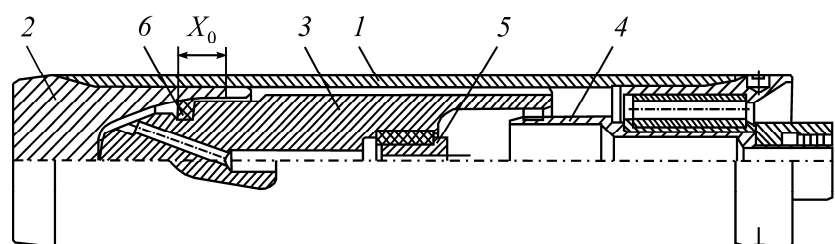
Общий вид пневмомолота: 1 — корпус; 2 — наковальня; 3 — ударник; 4 — задняя гайка с патрубком; 5 — сменный жиклер; 6 — упругий клапан
